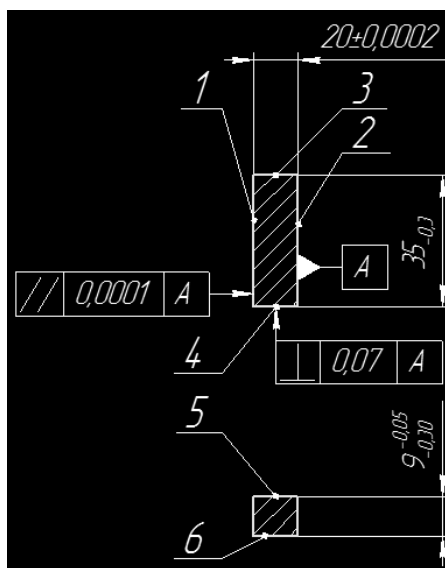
Размеры и допуски плитки плоскопараллельной концевой меры длины размером 20 мм
